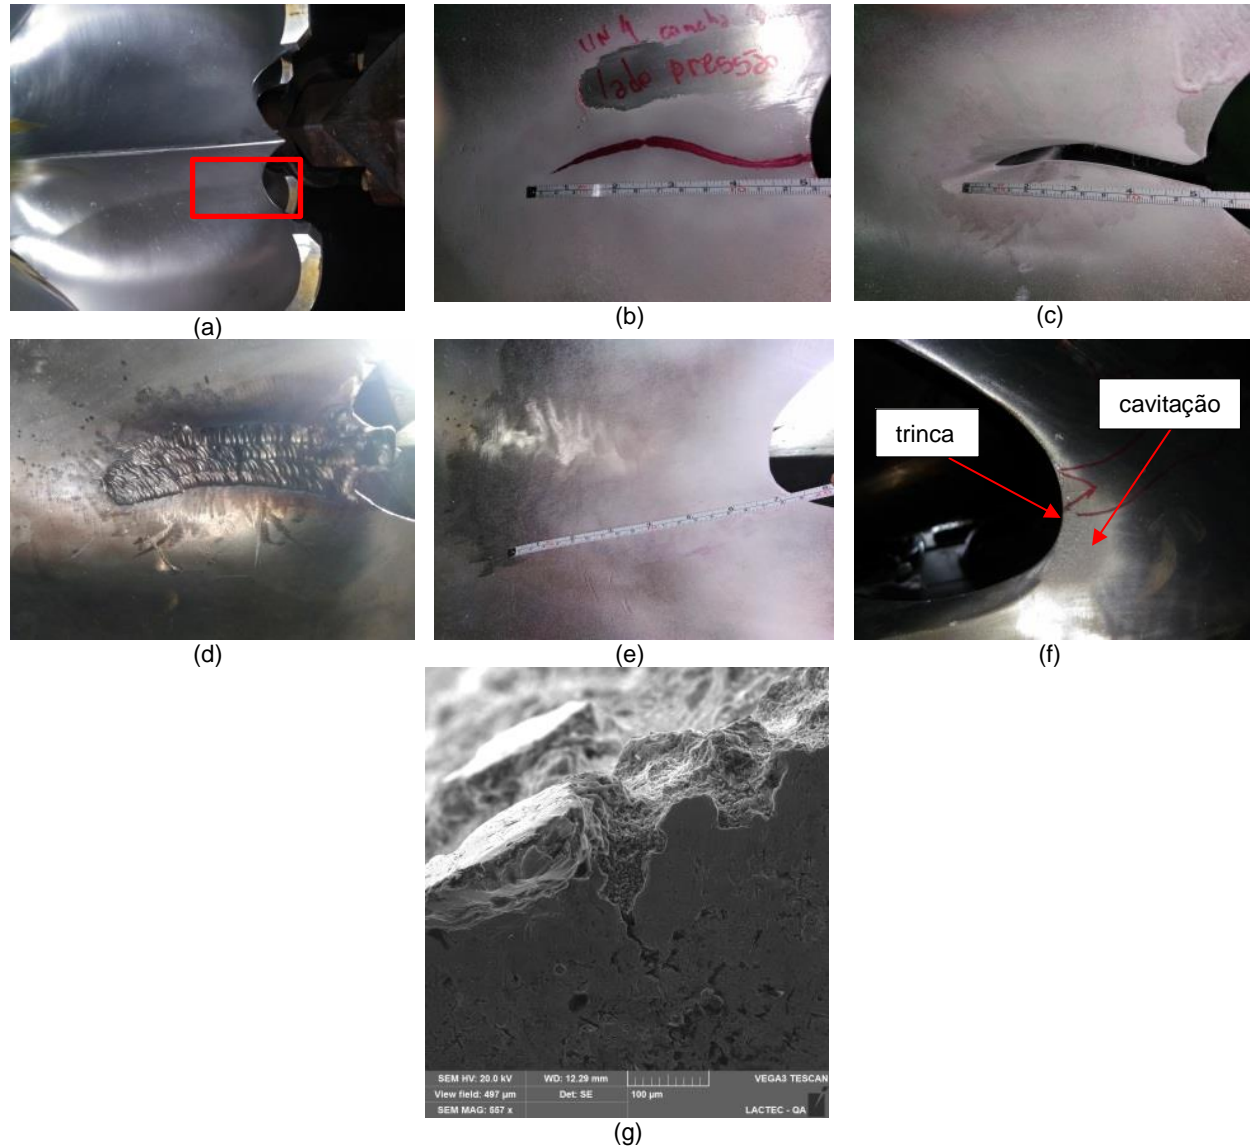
Recuperação de concha trincada em rotor da Usina Hidrelétrica Governador Parigot de Souza. (a) região da trinca, (b) evidência da trinca em ensaio por LP, (c) trinca eliminada e chanfro preparado para soldagem, (d) cordões de solda, (e) condição final da recuperação em ensaio por LP. A análise da falha foi feita com retirada de parte da trinca, (f) cavitação e corte de parte da trinca e (g) trinca nucleada em região de cavitação. O procedimento de recuperação desse tipo de trinca é resultado de PeD ANEEL (6).
